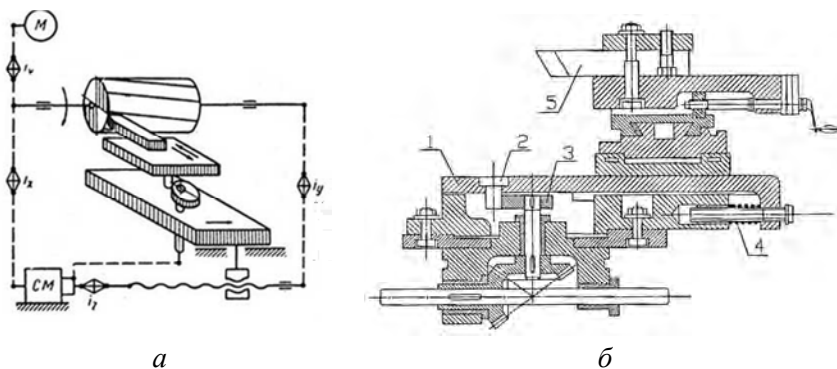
Структурно-кинематическая схема (а) и суппорт токарно-затыловочного станка (б):
